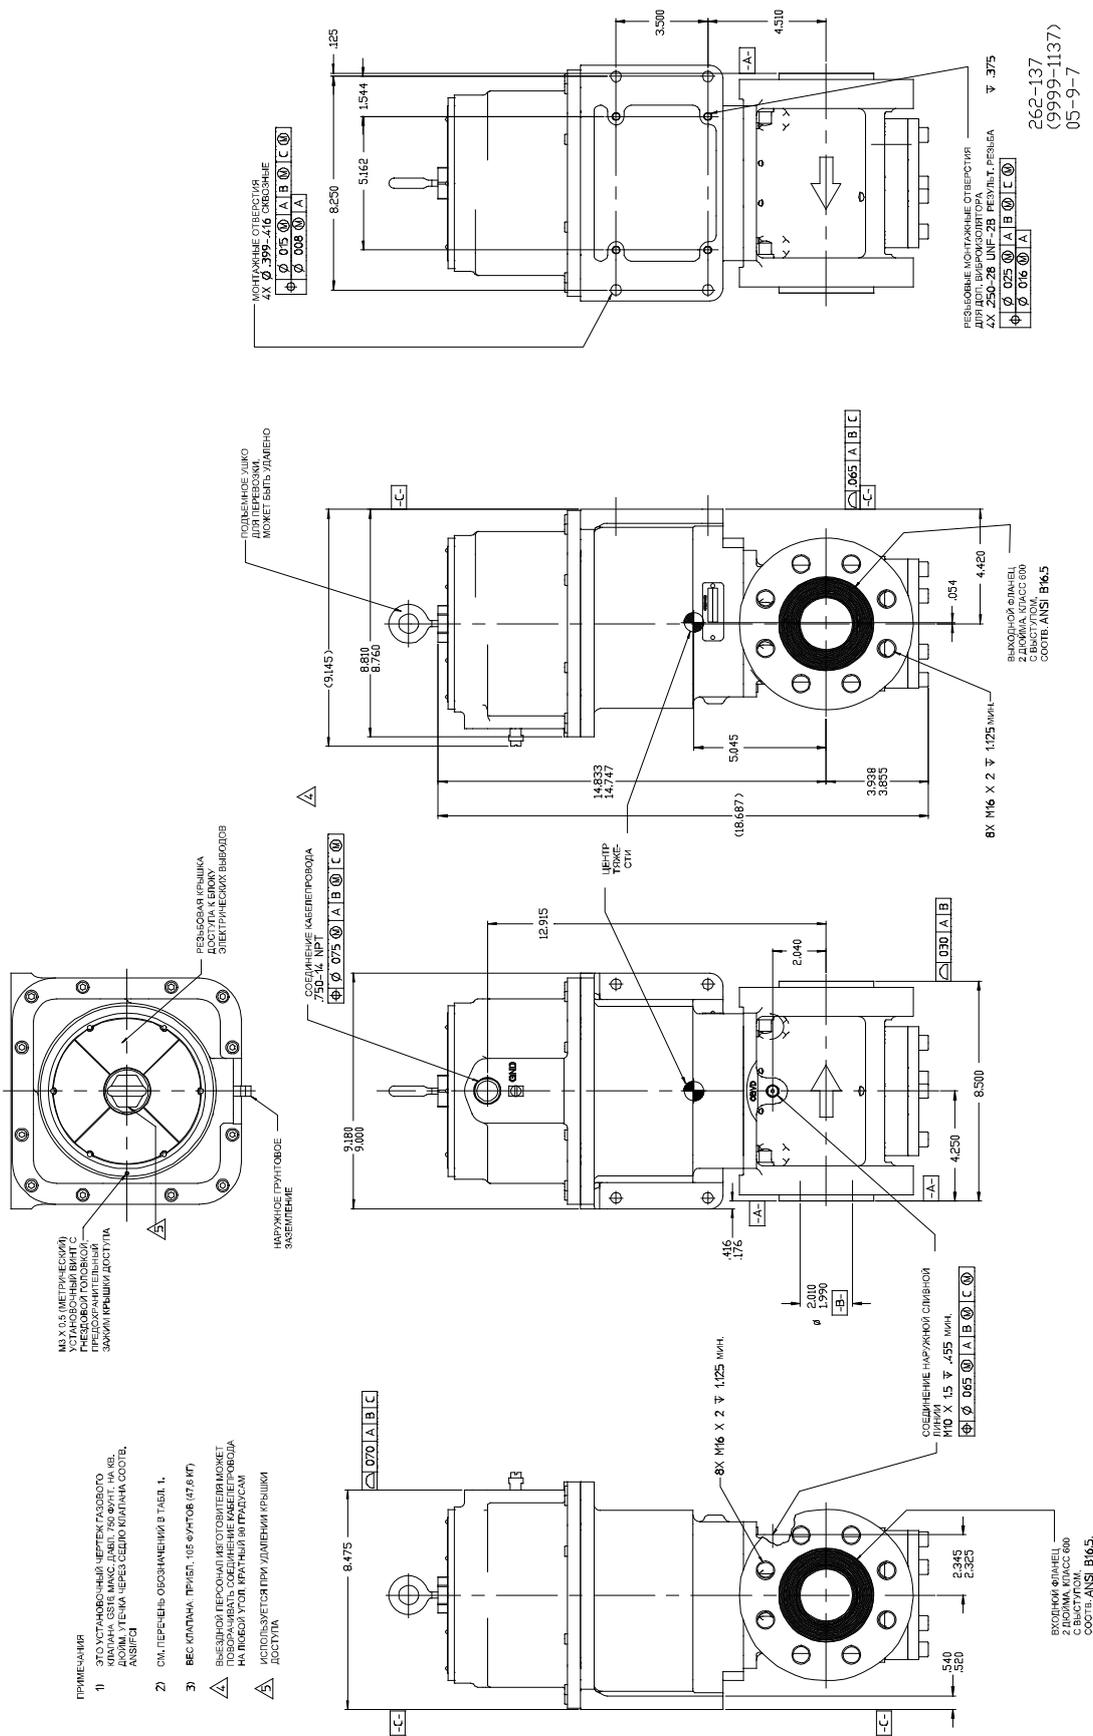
Контурный чертеж дозатора GS16 с метрическими отверстиями фланцев под болты (размеры указаны в дюймах)
